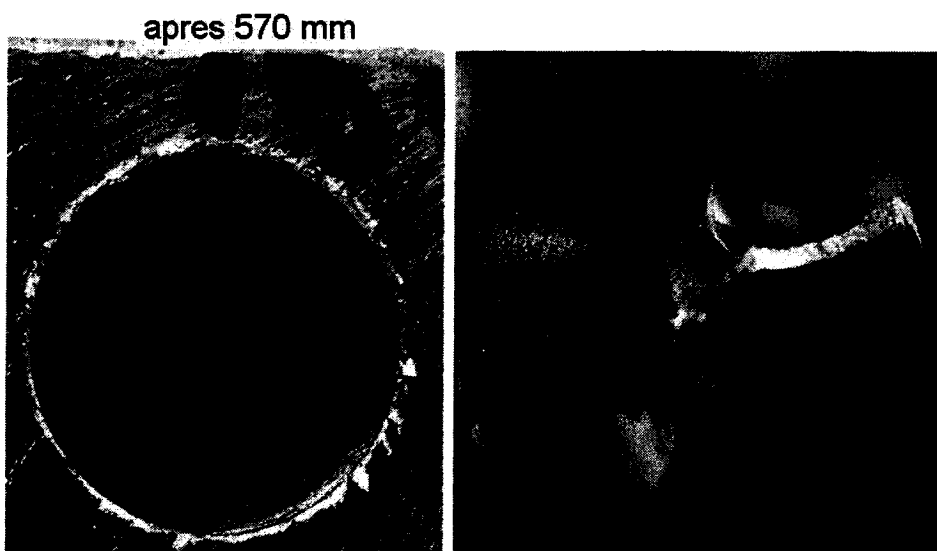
Formation des bavures par rapport à l'usure, foret carbure solide Guhring, avance 0.2 mm rev, 6000 rpm.
